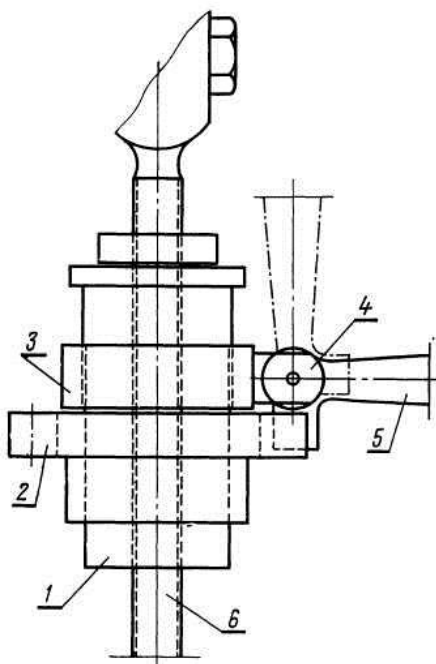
Схема вдосконалення механізму для регулювання зазору між вальцями:
